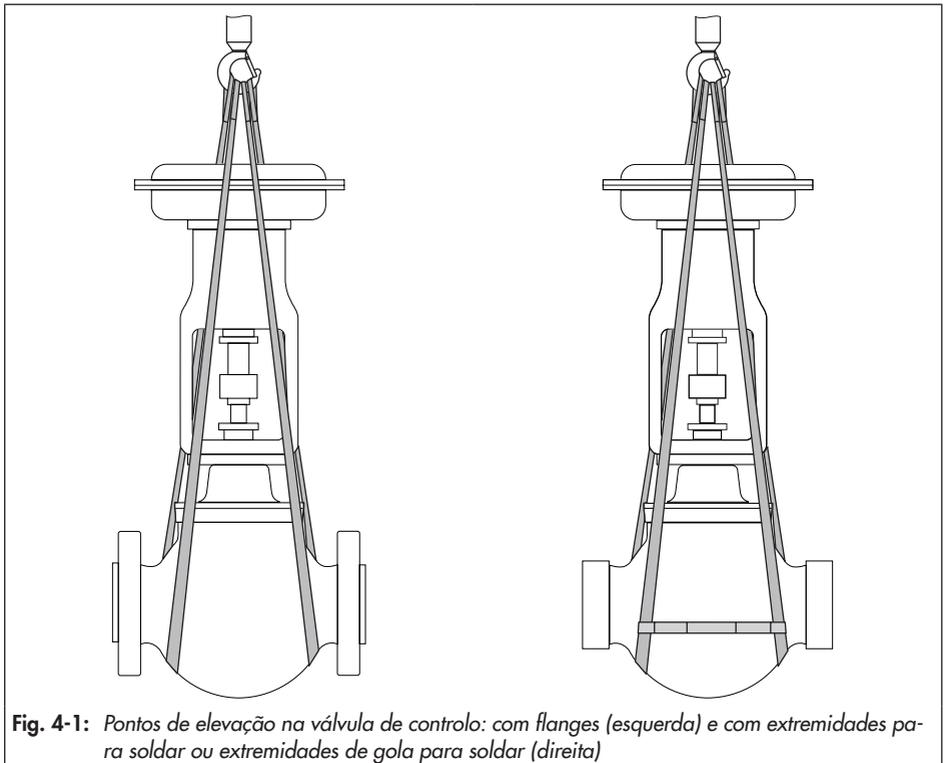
Pontos de elevação na válvula de controlo: com flanges (esquerda) e com extremidades para soldar ou extremidades de gola para soldar (direita)
